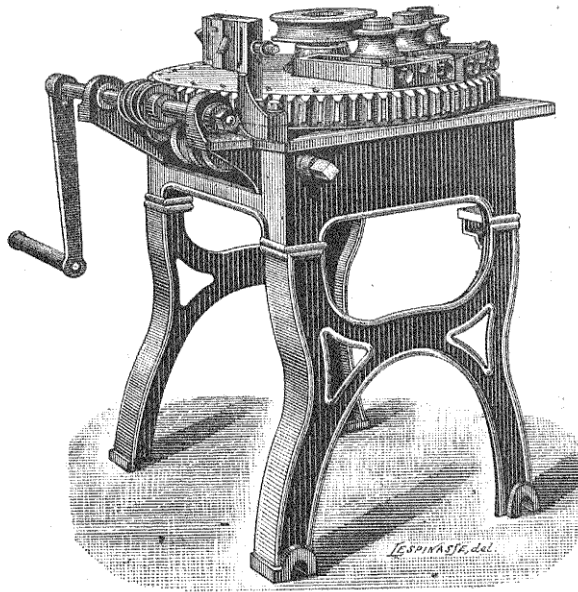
Machine Dard à cintrer les tubes à froid.
